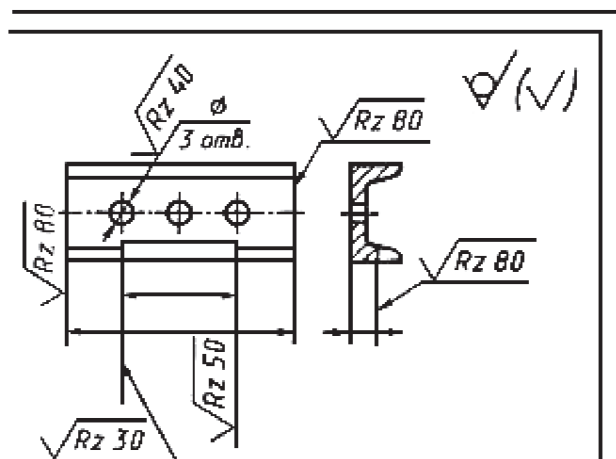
Обозначение шероховатости, одинаковой для части поверхности детали
